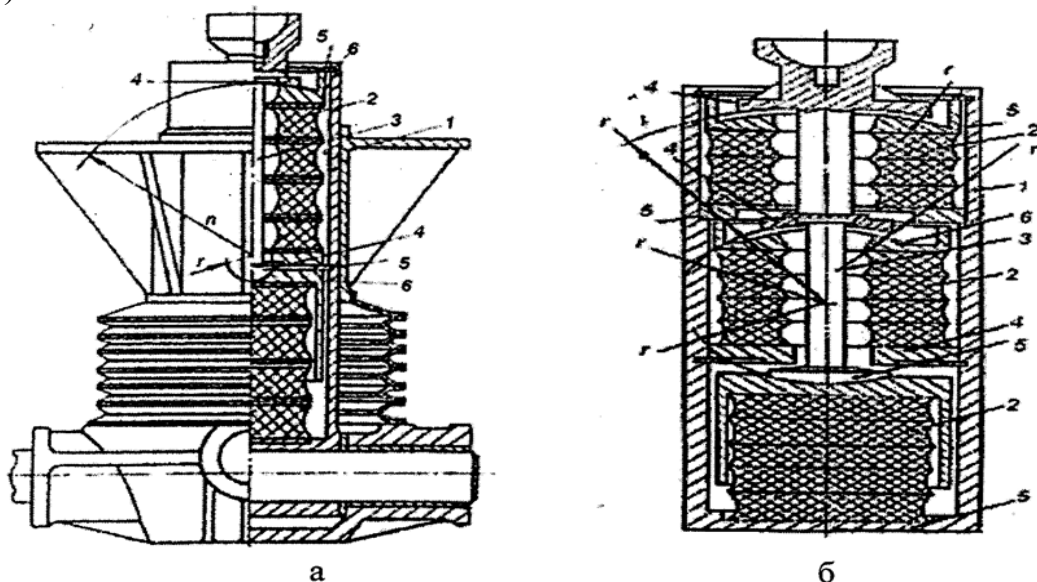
Пружний елемент підвіски транспортного засобу: 1 – корпус;
